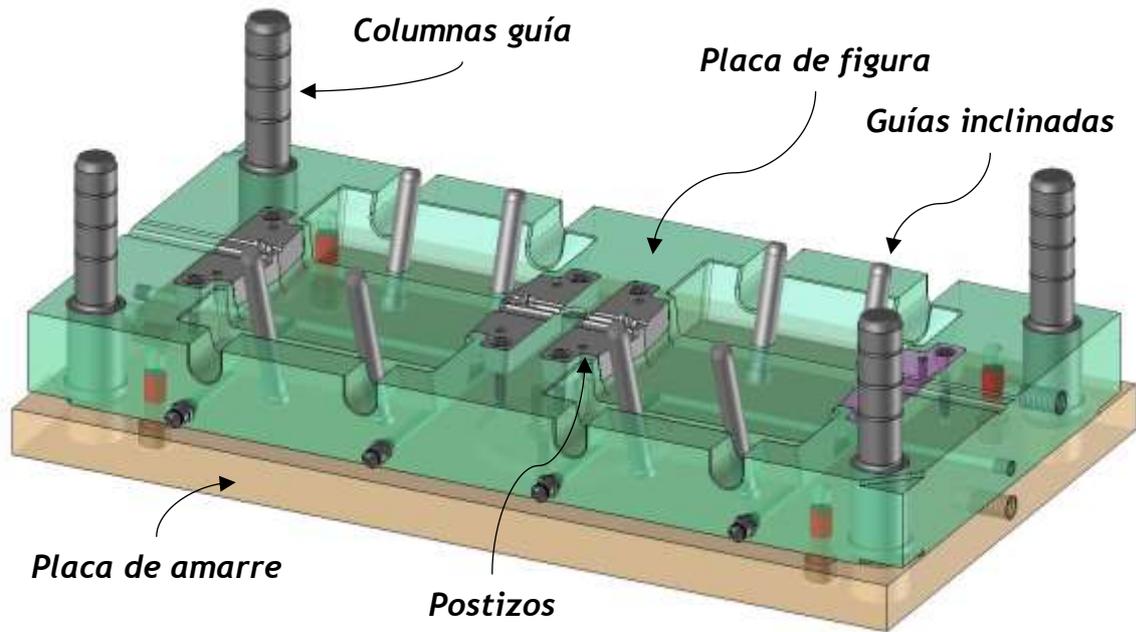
Vista trimétrica del lado de la inyección del molde.
